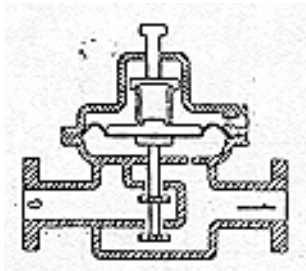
와 같이 Valve가 1차측에 있어, 입구압력이 Valve를 닫는 방향으로 작용하기 때문에 입구 압력이 높아지면 출구 압력이 어느 정도 낮아지게 된다. 중압조정기, 대형의 저압조정기 및 Out Valve type과 직렬연결하여 정밀 조정용 Pilot 조정기에 잘 이용된다.
